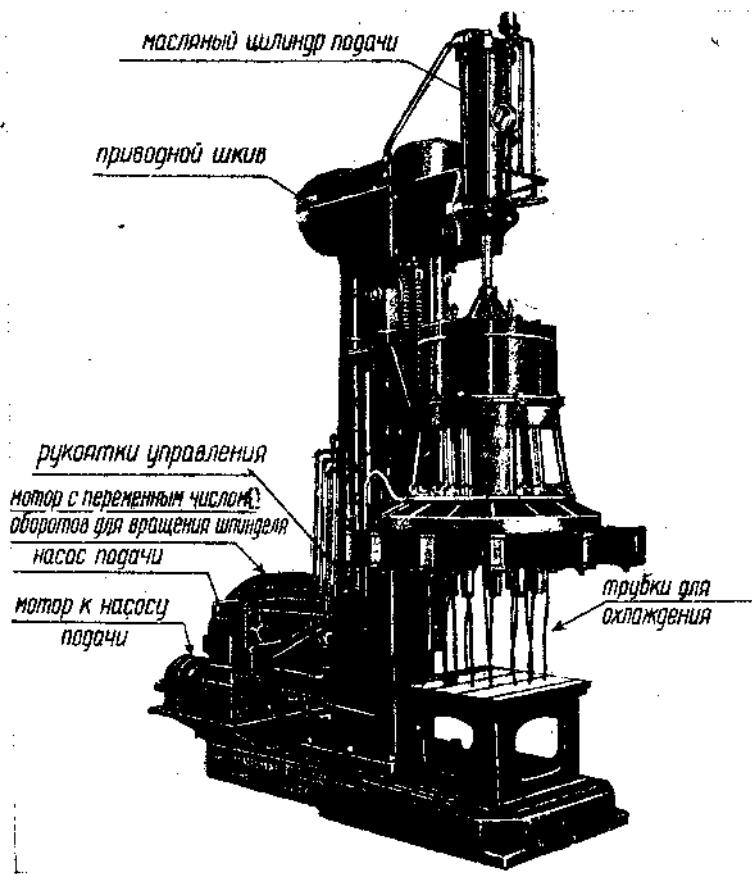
Многошпиндельный вертикальный сверлильный станок.
